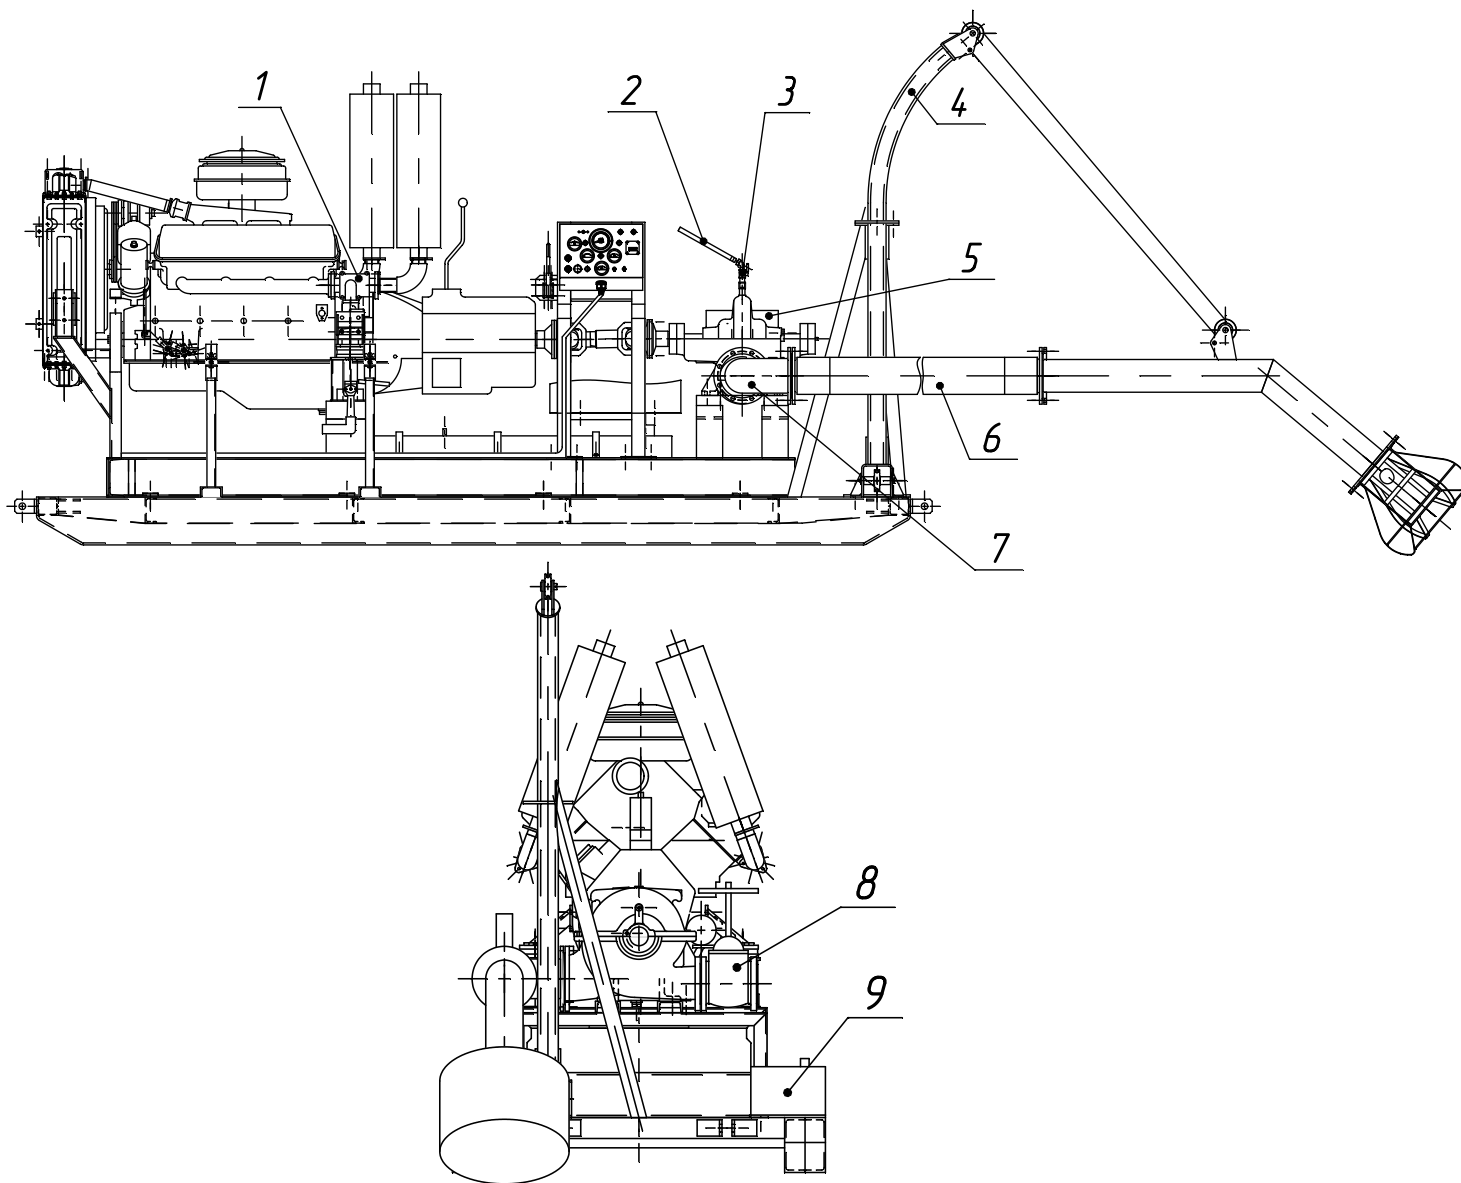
Общий вид агрегатов типа ДНА-П
